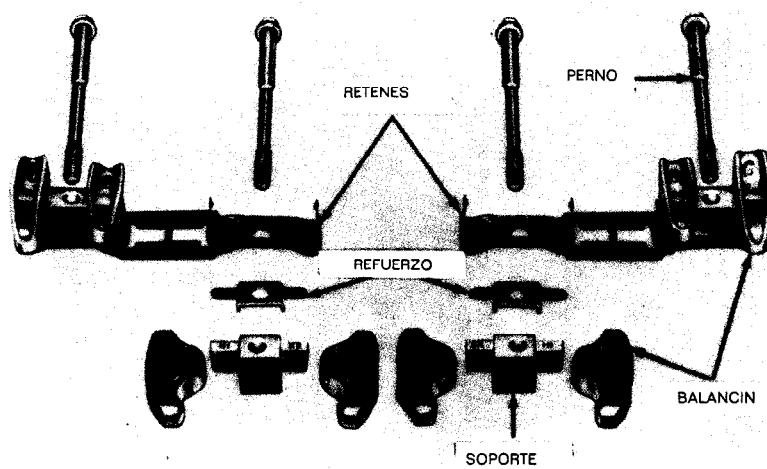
Balancines, soportes y retenes (Cadillac Motor Car Division of General Motors Corporation).
